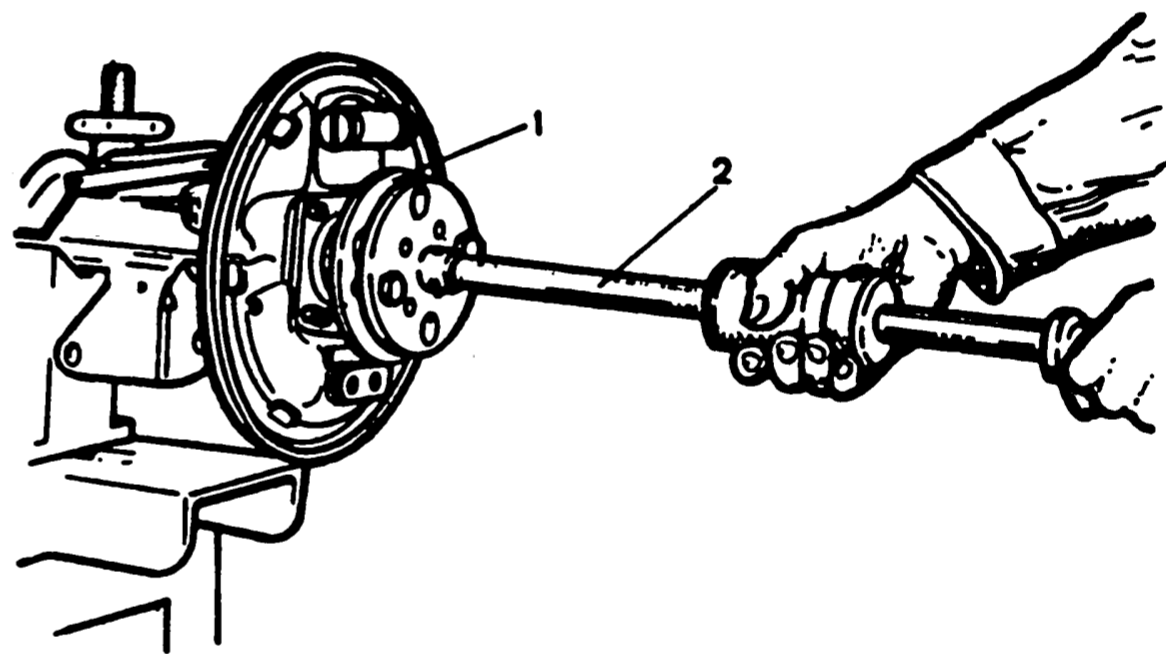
Выпрессовка полуоси с помощью съемника 67.7801.9516: 1 - полуось; 2 - ударный съемник
